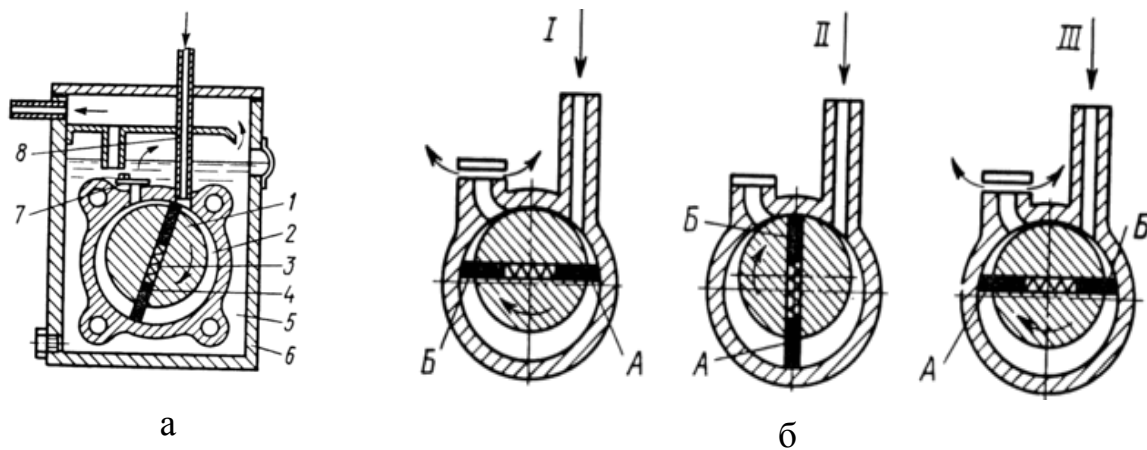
Пластинчато-роторний механічний насос: а – устрій; б-принцип дії; 1– ротор, 2– камера, 3– пружина, 4– пластина, 5– масляна ванна, 6 – корпус, 7 – вихлопний клапан, 8 – впускний патрубок
